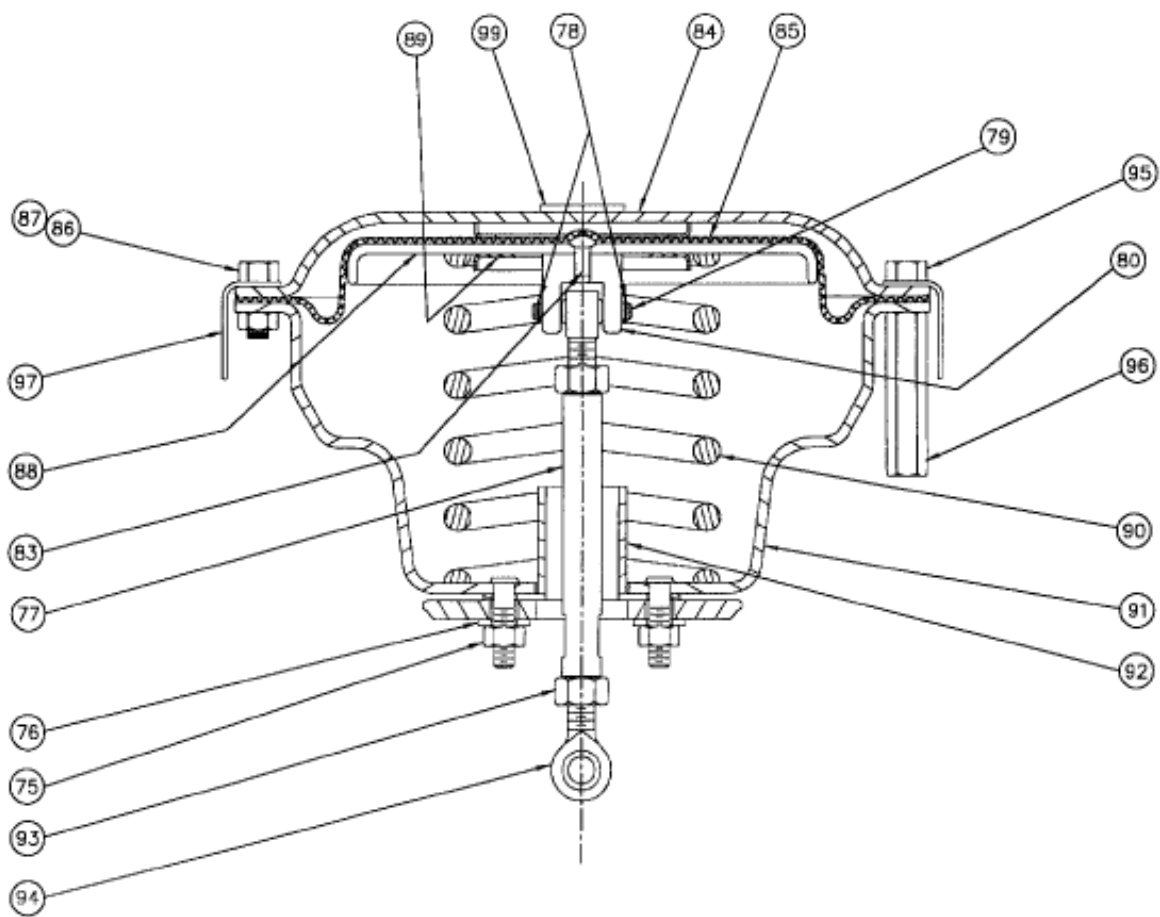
Ensamblaje general del actuador, tamaños de actuador B y C
